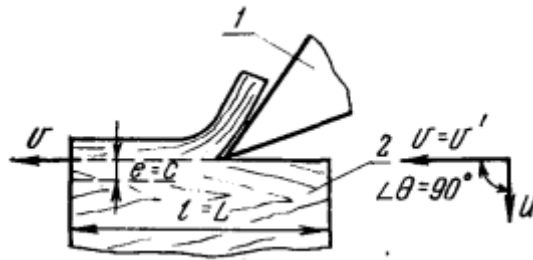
Схема строгания: 1 – резец; 2 – заготовка
